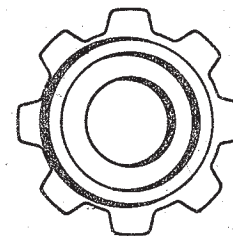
Способ облегчения упорной тарелки клапанной пружины
